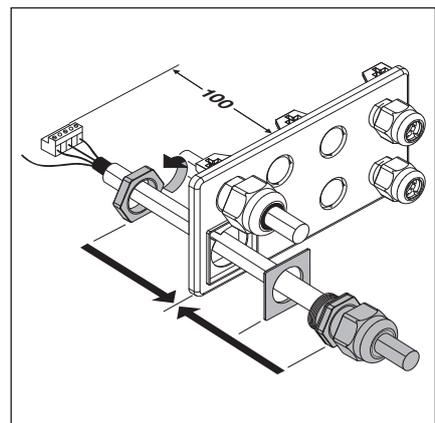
Endmontage der Verschraubungsflanschplatte
